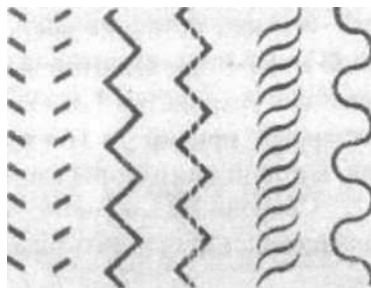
Виды ультразвуковых сварных швов
